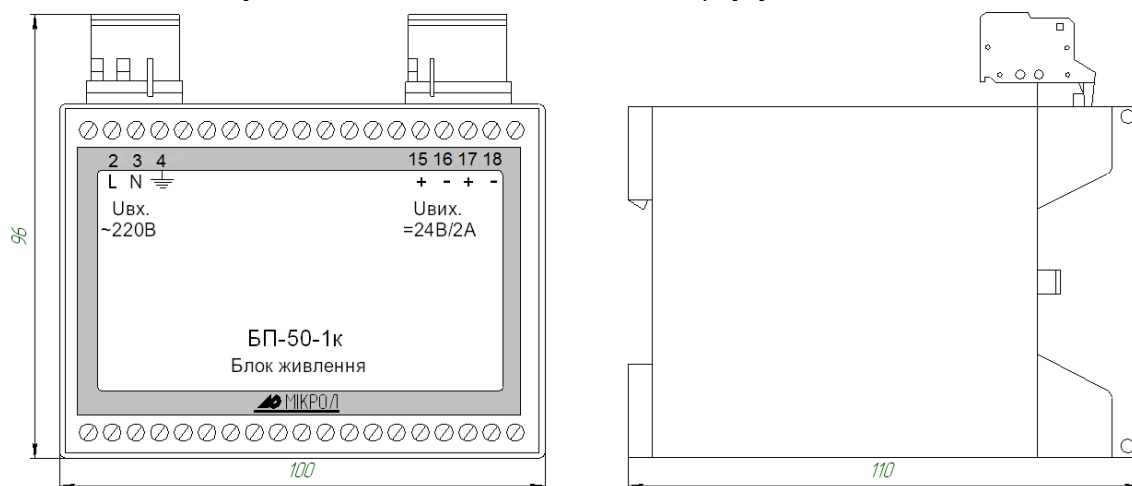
Зовнішній вигляд та габаритні розміри блока живлення БП-50
